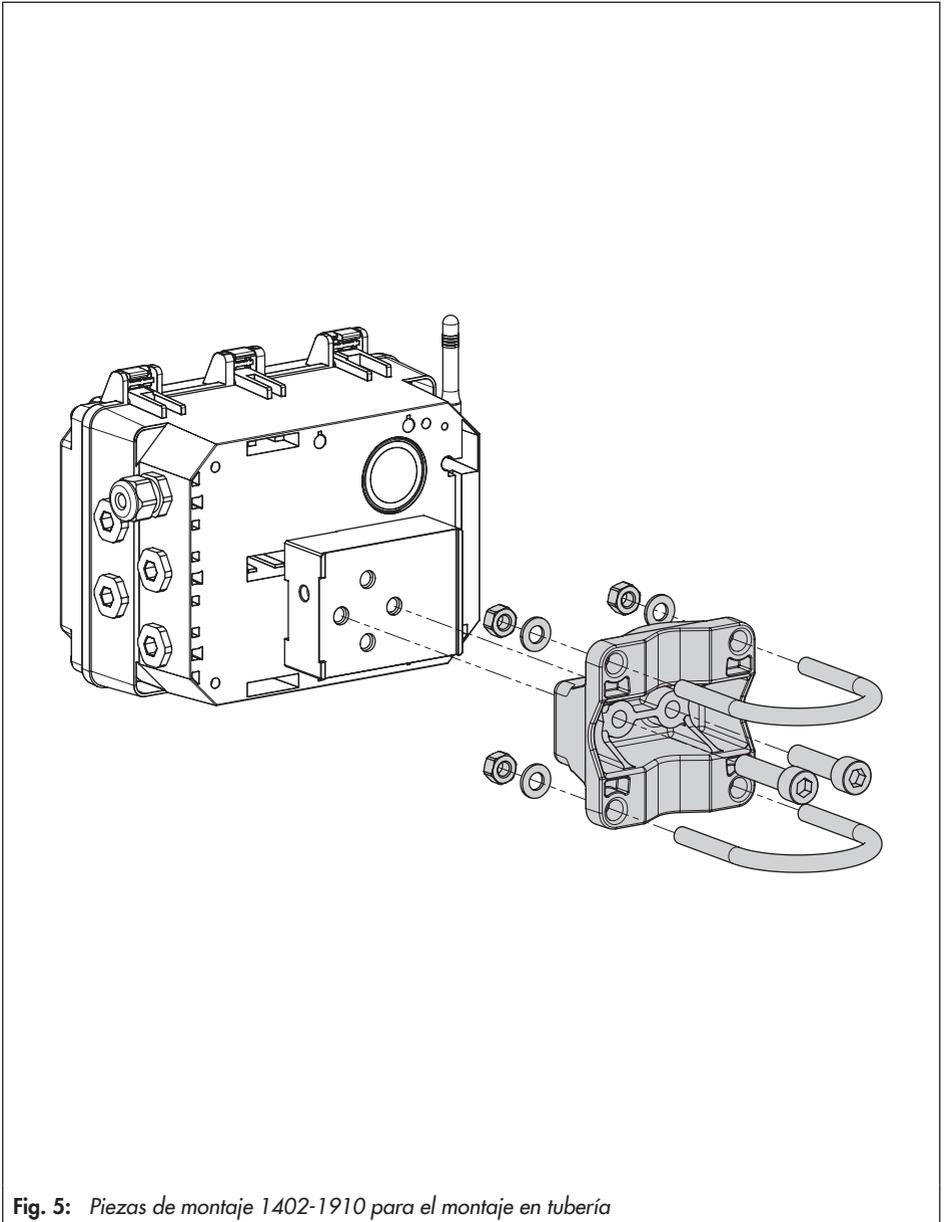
Piezas de montaje 1402-1910 para el montaje en tubería
